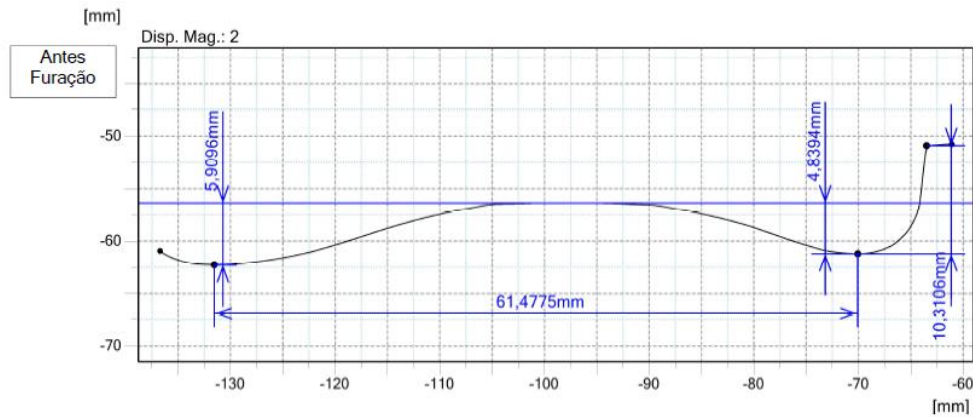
Perfil desenhada pelo perfilómetro da chapa.
